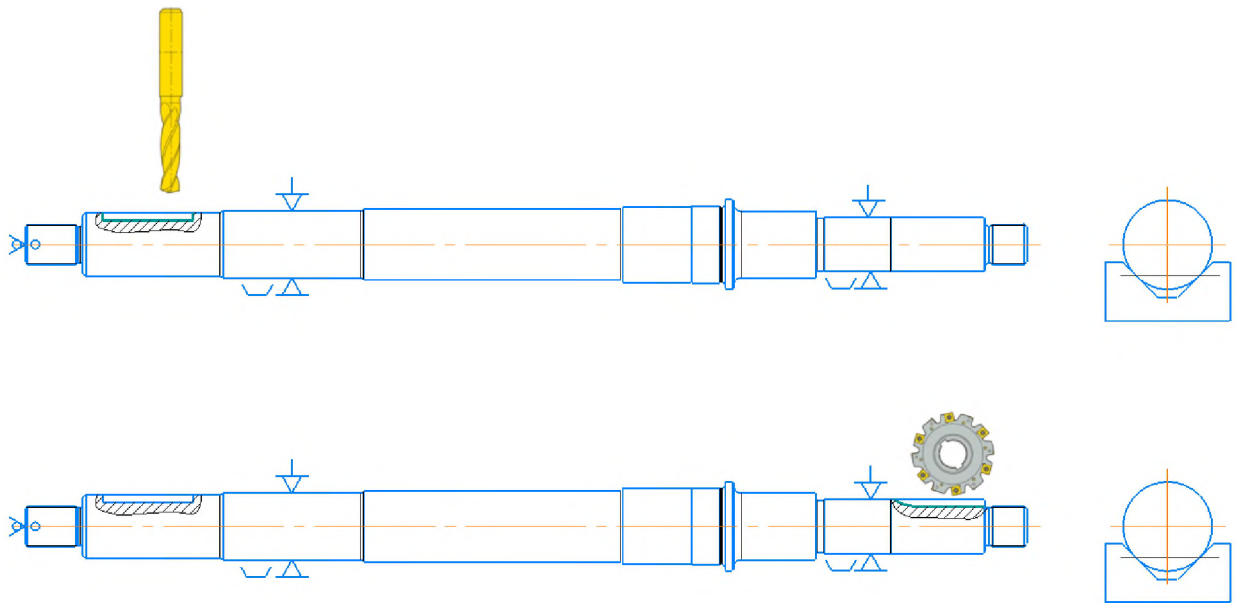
Технологічна схема базування третього варіанту встановлення заготовки (нахил фрезерної головки)
